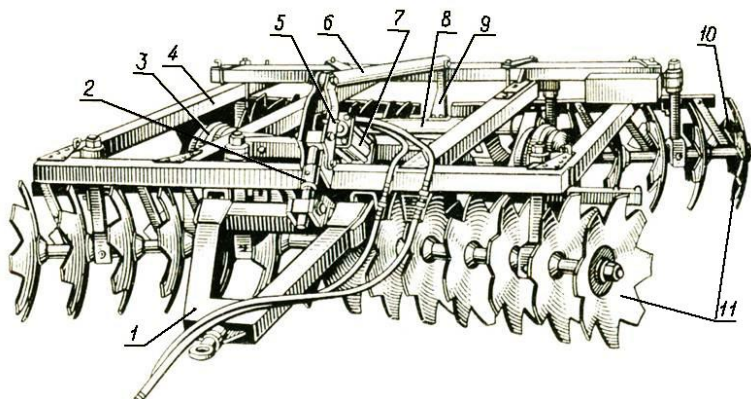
Борона дисковая тяжелая Л-113-02 (БДТ-3): 1 – прицепное устройство; 2 – регулировочный винт; 3 – колесо; 4 – рама; 5 – рычаг; 6 – тяга; 7 – гидроцилиндр; 8 – коленчатая ось, 9 – кулак; 10 – чистик, 11 – батареи
